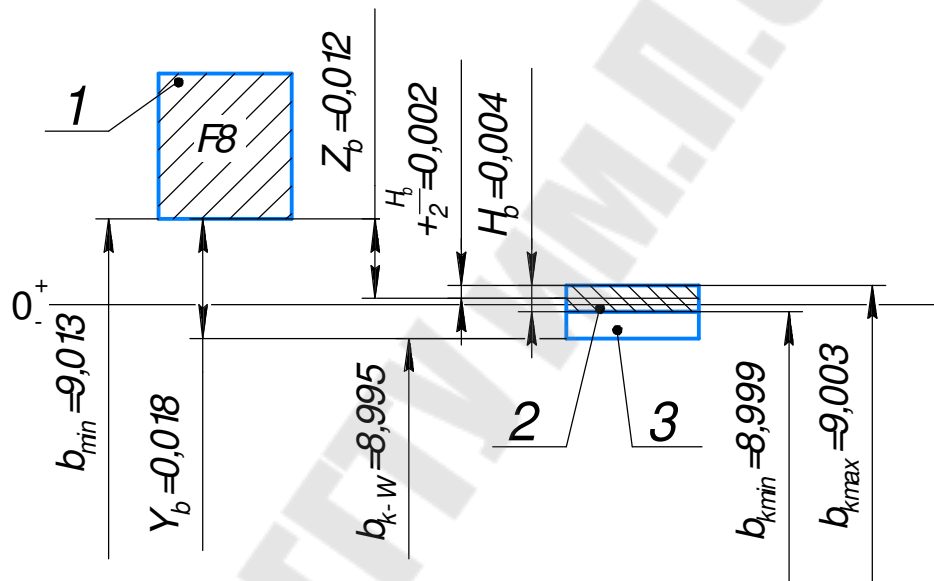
Схема расположения полей допусков, нецентрирующего размера b калибра-пробки: 1 – поле допуска размера b втулки; 2 – поле допуска на изготовление калибра-пробки; 3 – поле износа калибра-пробки.
